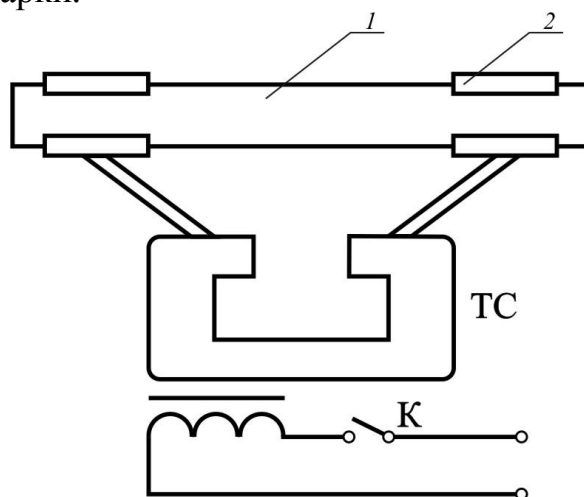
Схема установки для стыковой сварки: 1- деталь; 2- зажимы
